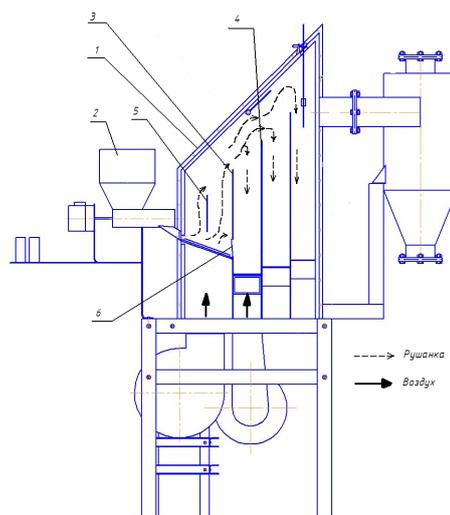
Схема лабораторно-экспериментального пневмосепаратора для разделения зернового материала: 1 – корпус; 2 – шнековый дозатор; 3 – задняя стенка сепарирующего канала; 4 – стенка осадительного канала; 5 – барьер, выравнивающий зерновой поток; 6 – перегородка
